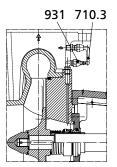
Сборочный чертеж, диаметр вала 55 мм
